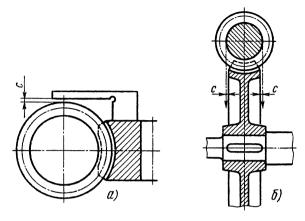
Проверка установки червячного колеса: a — специальным шаблоном: δ — отвесами
